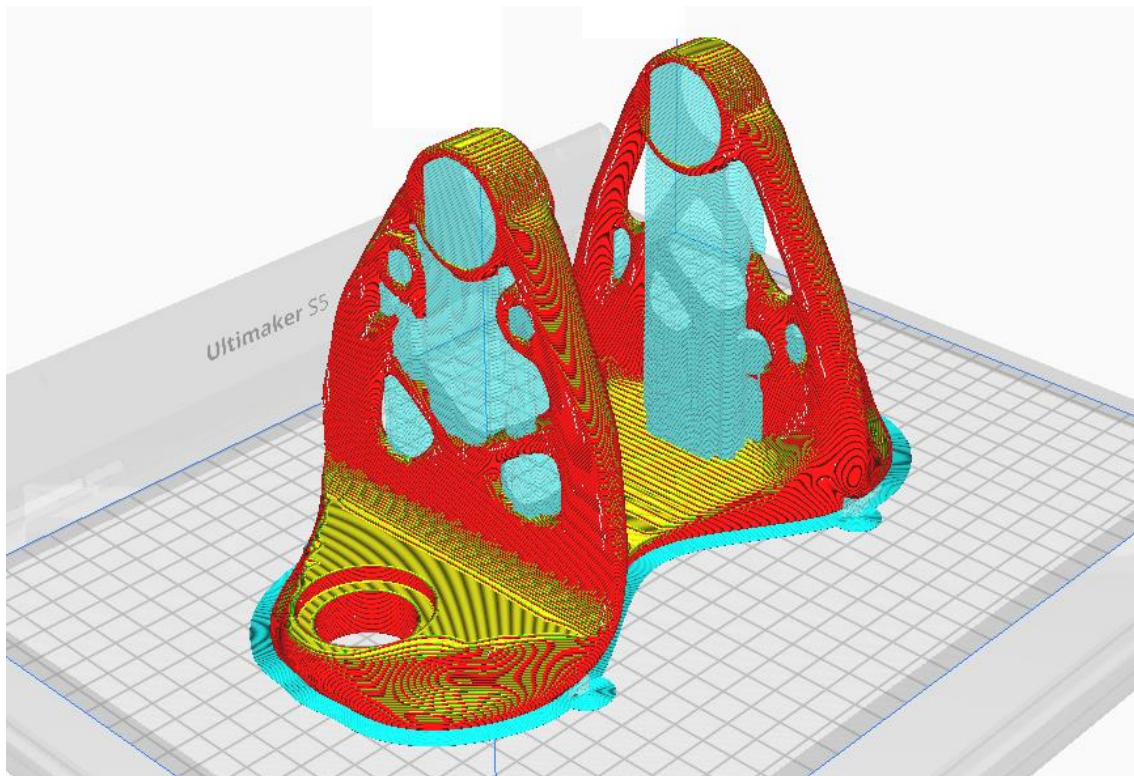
Detalle de la cantidad de soporte que requeriría la pieza
